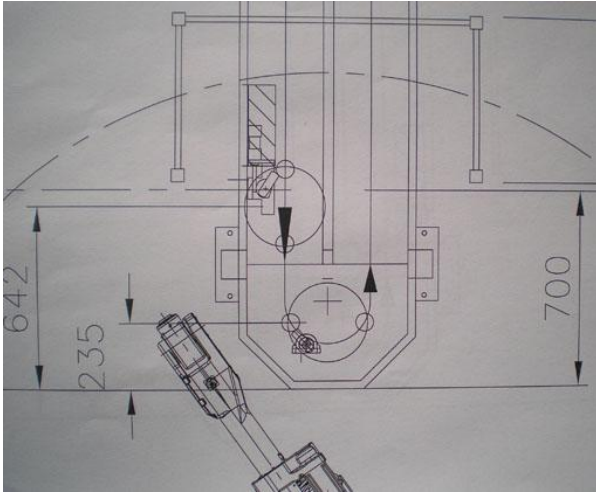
Configurazione del nastro inadatta: all'estremità ha spazio un solo pallet, e servirebbe che il nastro entrasse maggiormente nell'area di lavoro.
